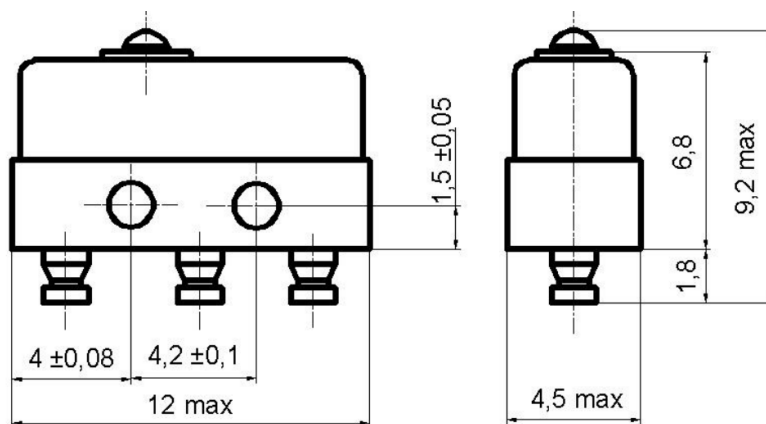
Габаритные и установочные размеры микропереключателя МП12
